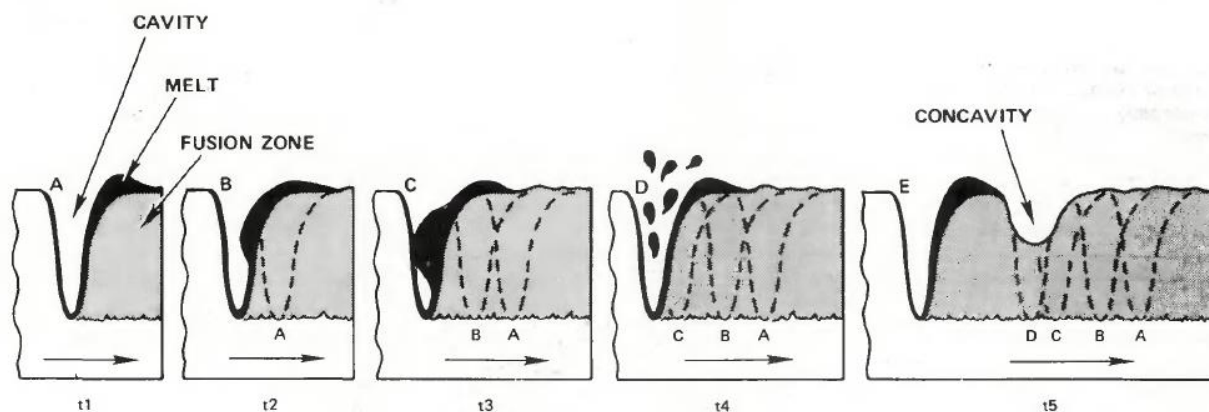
Возможный механизм образования дефектов в МШ азотсодержащей стали 21Cr-6Ni-9Mn-0,4N, показывающий нестабильное поведение полости сварного шва в разные промежутки времени t1-t5 [43].
